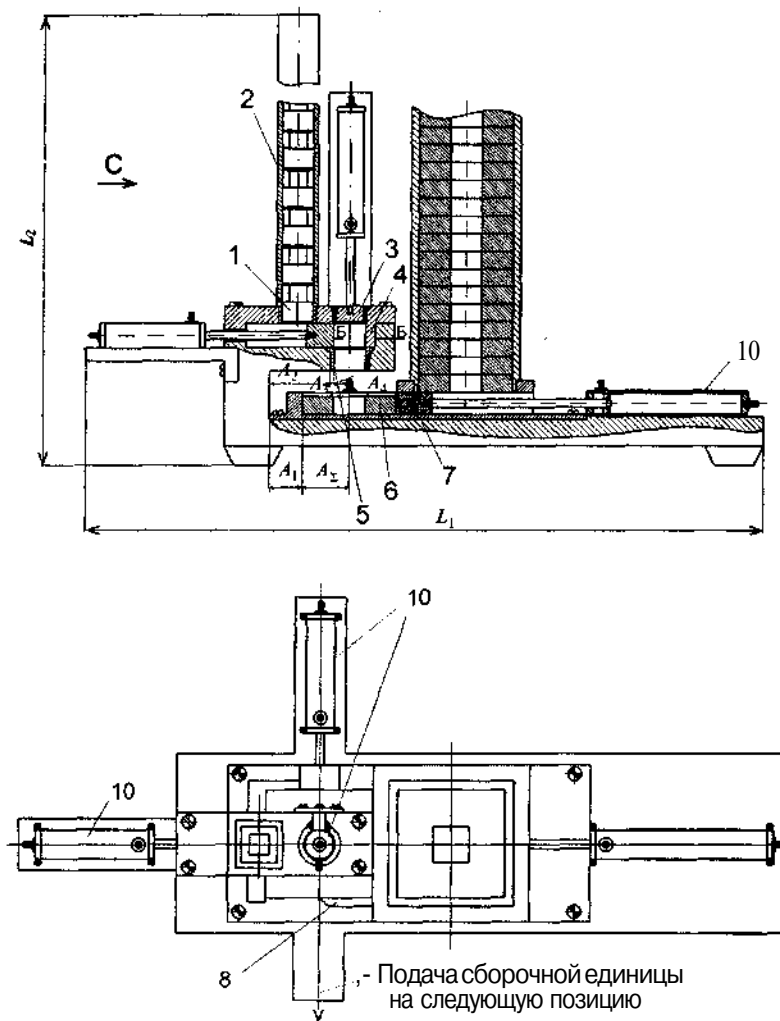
Приспособление для сборки штифта с основанием в автоматическом режиме
